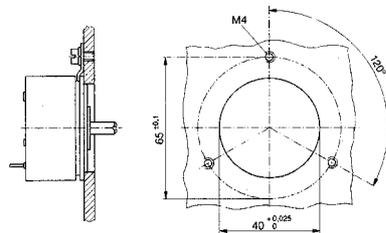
Bohrplan für Befestigung mit 3 Spannkammern.
